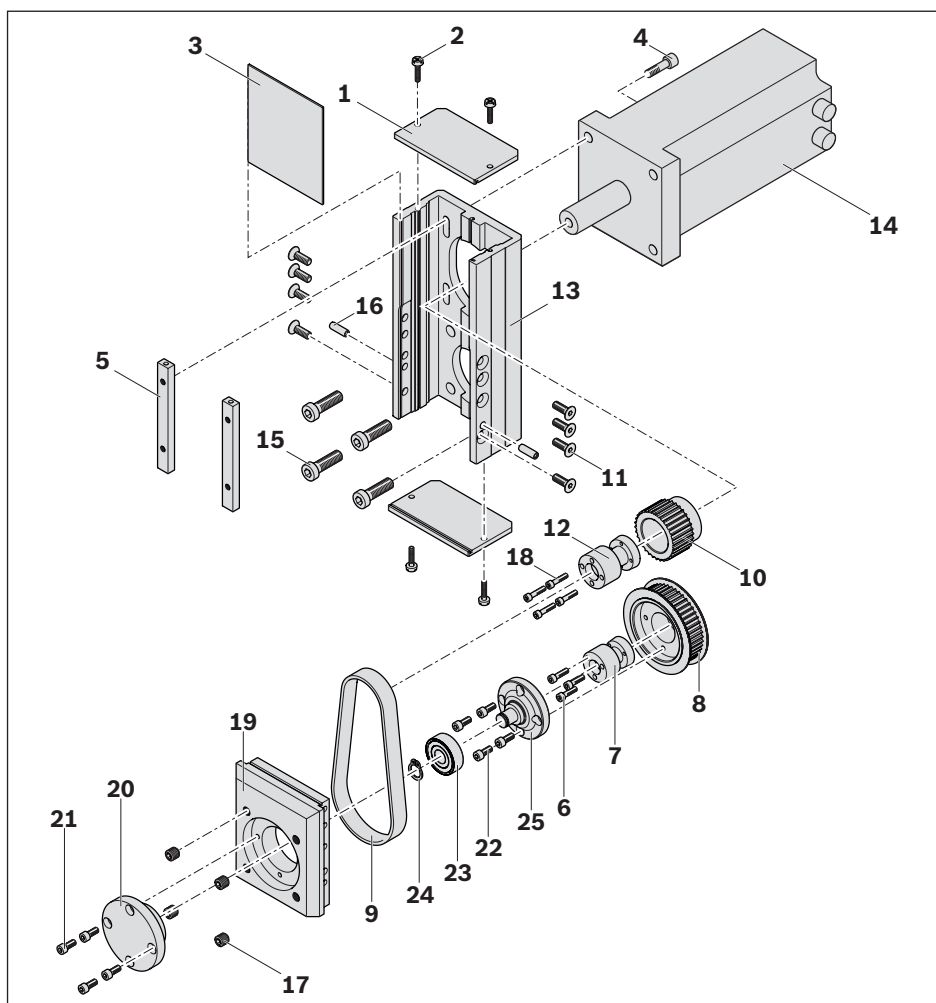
Desmontaje del motor y de la transmisión por correa dentada con contra-apoyo
